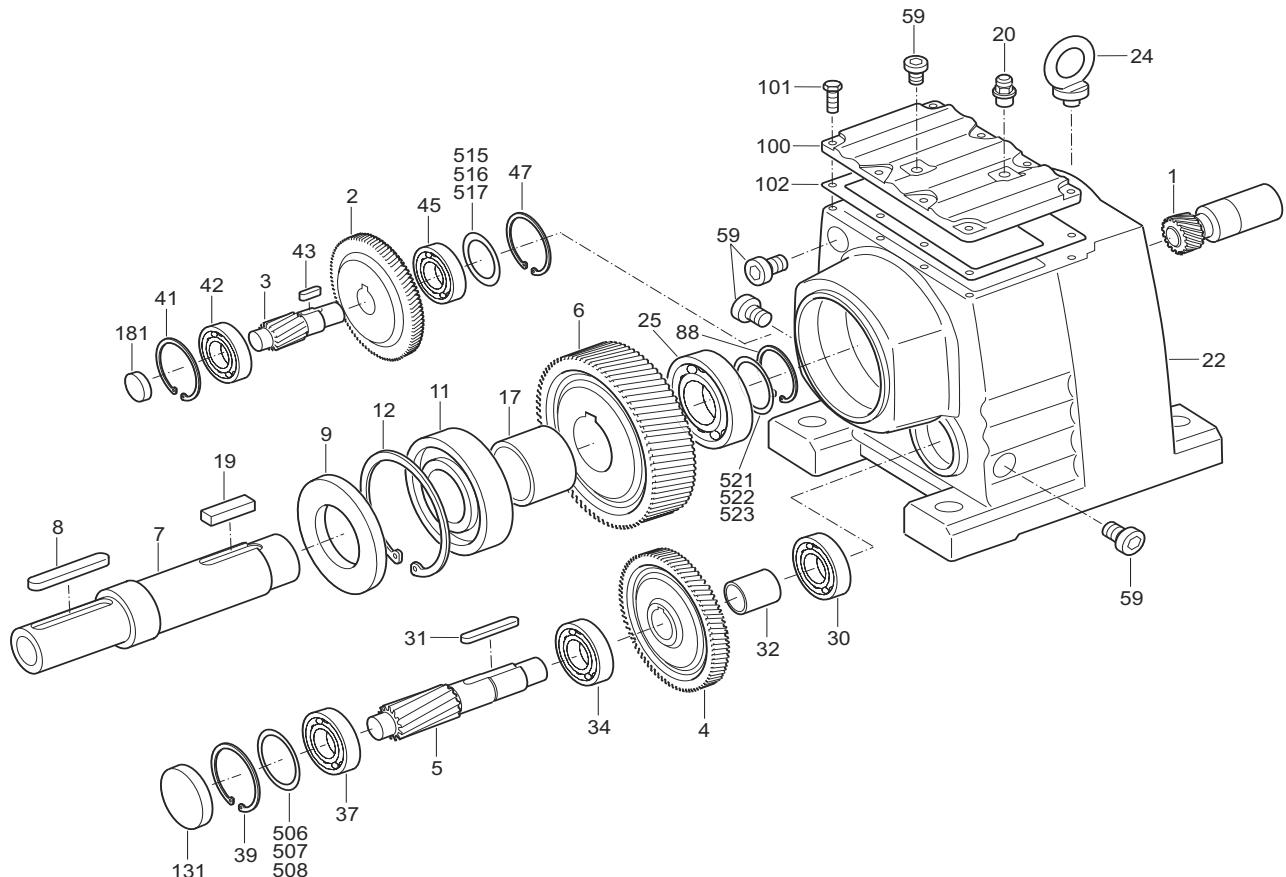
Prinzipieller Aufbau Stirnradgetriebe
